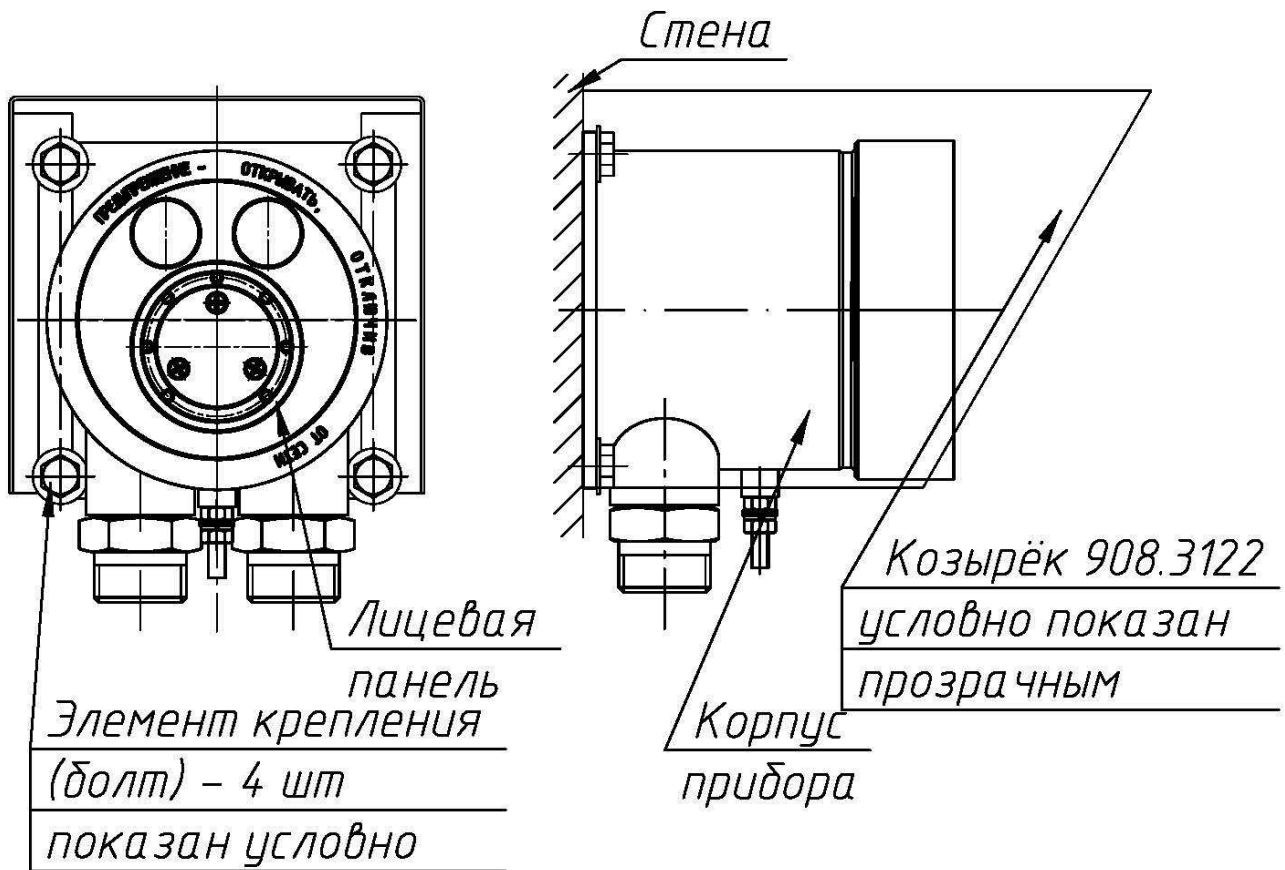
Чертёж козырька 908.3122 для оповещателей ExОПЗС
